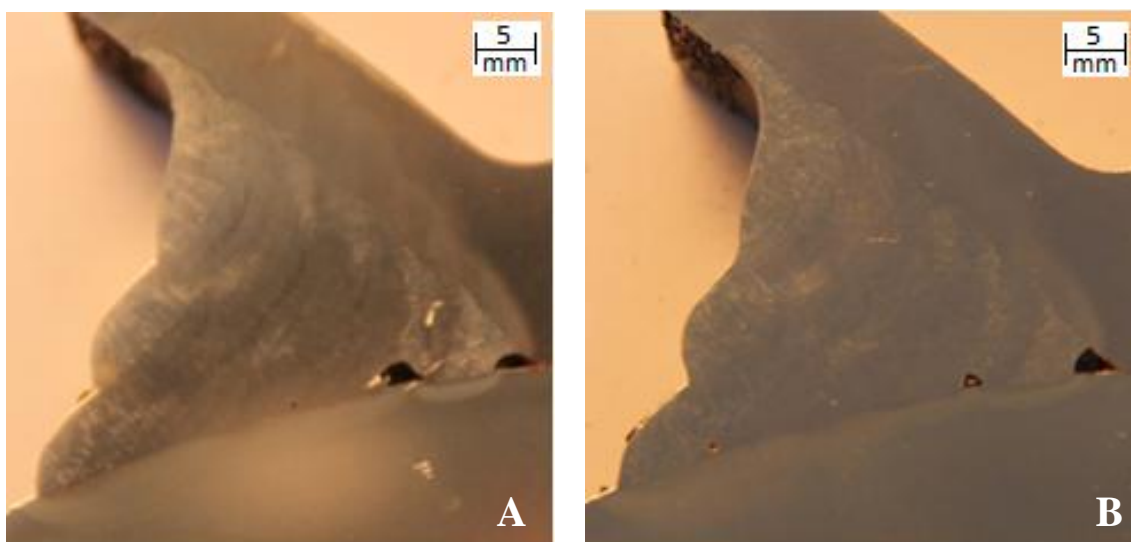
Macrografias do corpo de prova soldado com o processo FCAW
